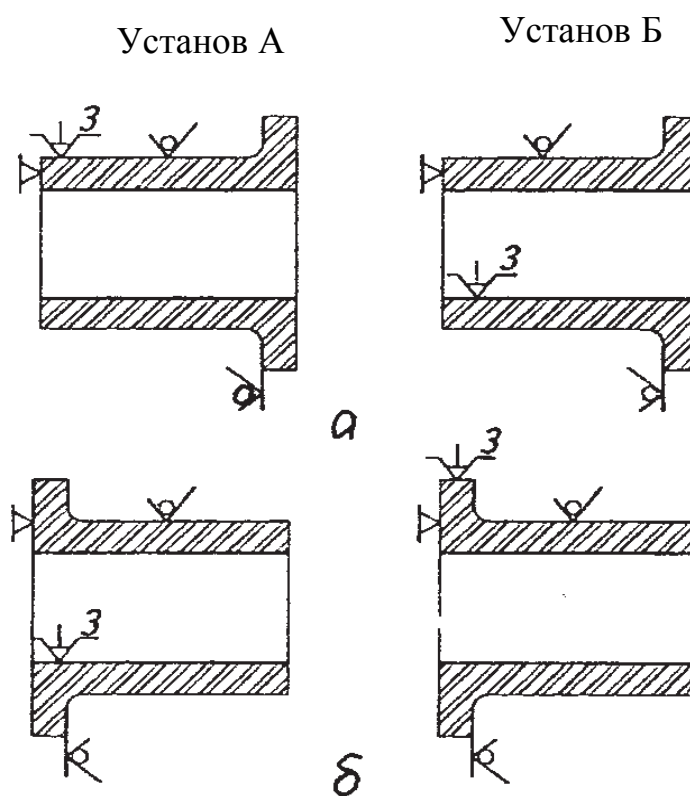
Схемы обработки втулки, наружный диаметр которой не требует обработки:
